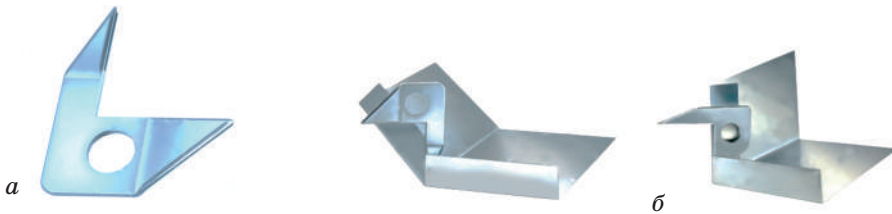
Кутозгин: а — загальний вигляд; б — формування покрівельних конвертів
